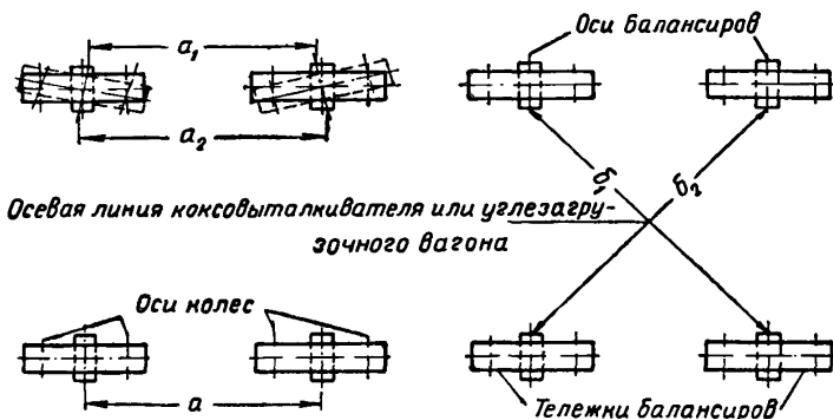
Схема проверки осей балансиров тележек коксовыталкивателя и углезагрузочного вагона
